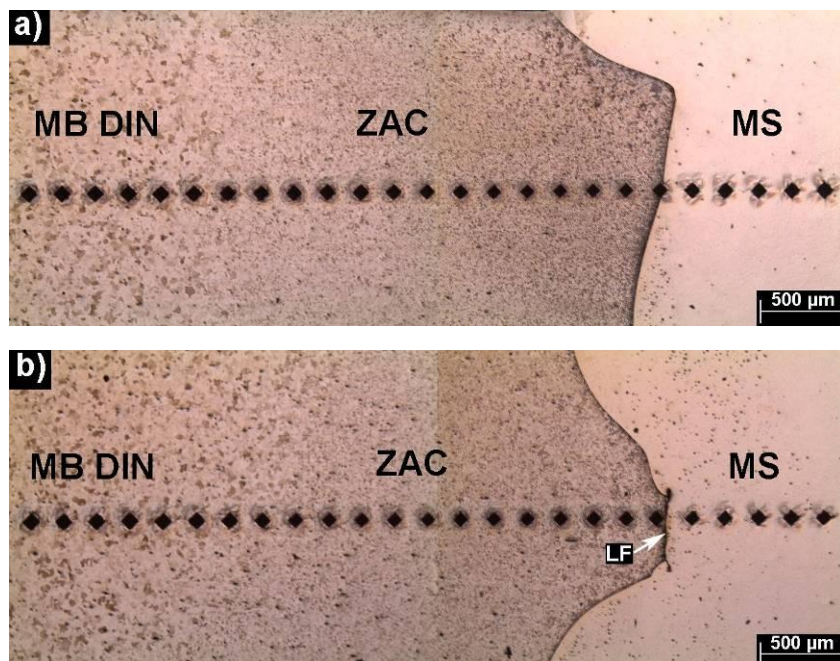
Macrografias da solda dissimilar DPI após o TT: (a) superfície do tubo; (b) centro da espessura. Ataque químico: Nital a 3%.
